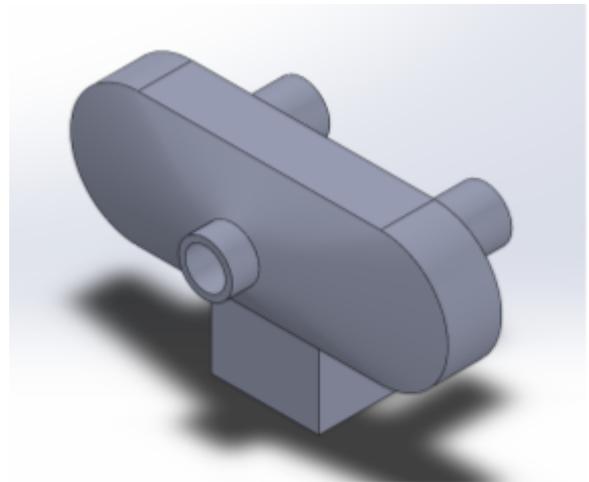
vue isométrique de derrière de la fiche des capteurs en modèle 3D
